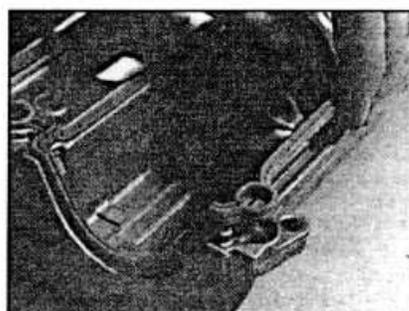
С.5. Установка прокладки в канавку крышки головки блока цилиндров.
